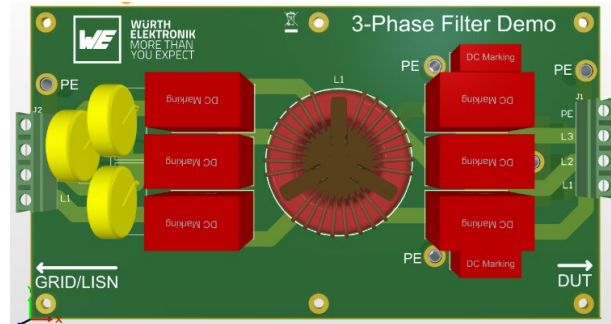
3D Top Ansicht 3-Phasen-Filter-PCB.
